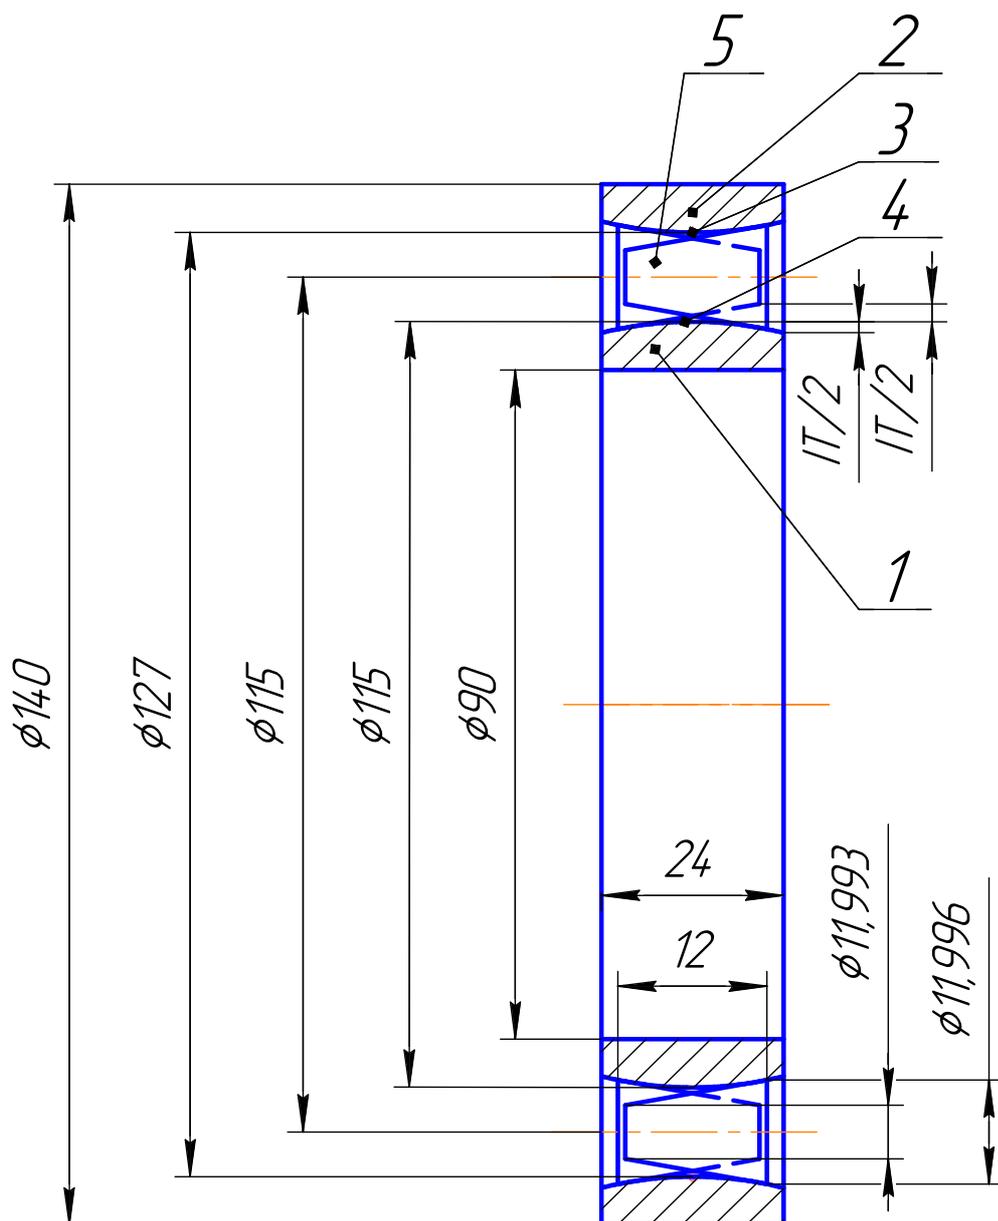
Вид тел поверхностей контакта тел и дорожек качения на поперечном сечении однорядного одноярусного беспараторного подшипника:
